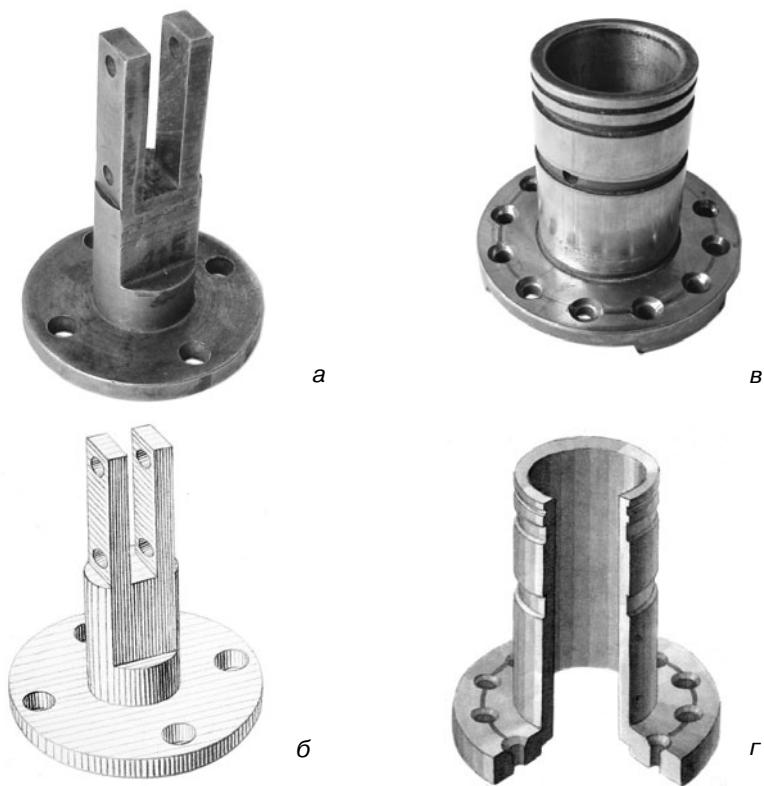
Рисование деталей, обработанных на металлорежущих станках:
